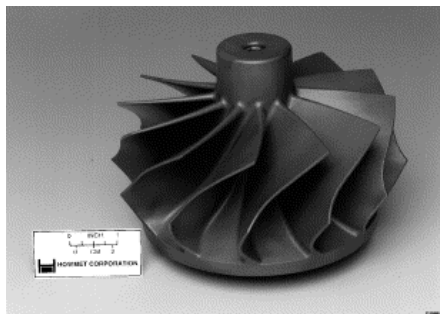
Turbina em TiAl para a zona quente do turbocompressor obtida por fundição [11].
